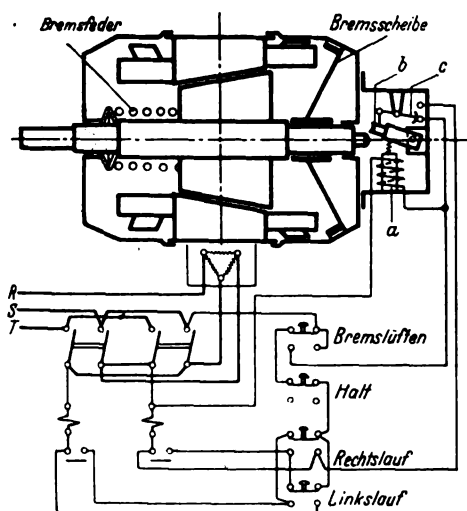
Verschiebeankermotor mit angebautem Bremslüftgerät.
